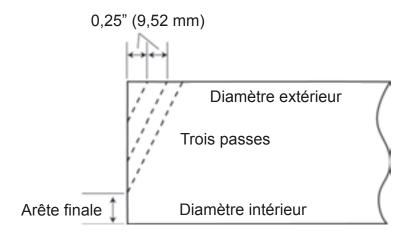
Le dessin illustre l'usinage d'un chanfrein droit en plusieurs passes. Réglez la profondeur du porte-outil à environ 1/4" (6,35 mm) en arrière le long du diamètre extérieur du tuyau pour chaque passe.
